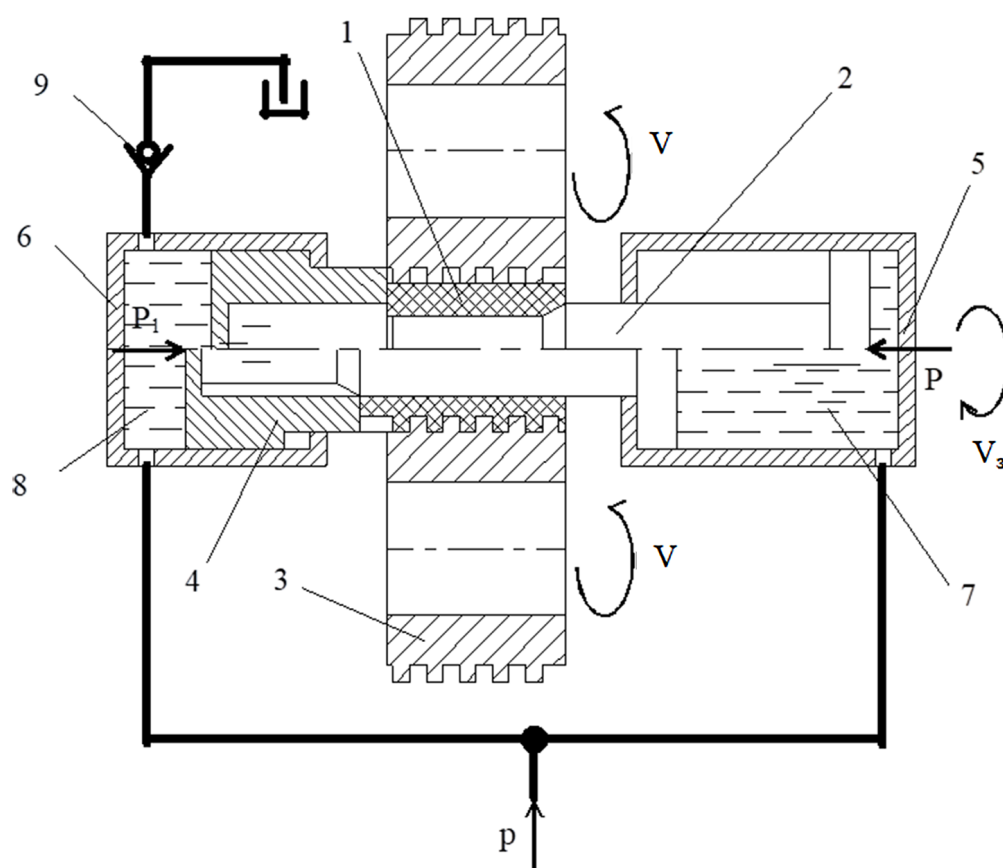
Схема накатывания упорной резьбы на полую заготовку:
